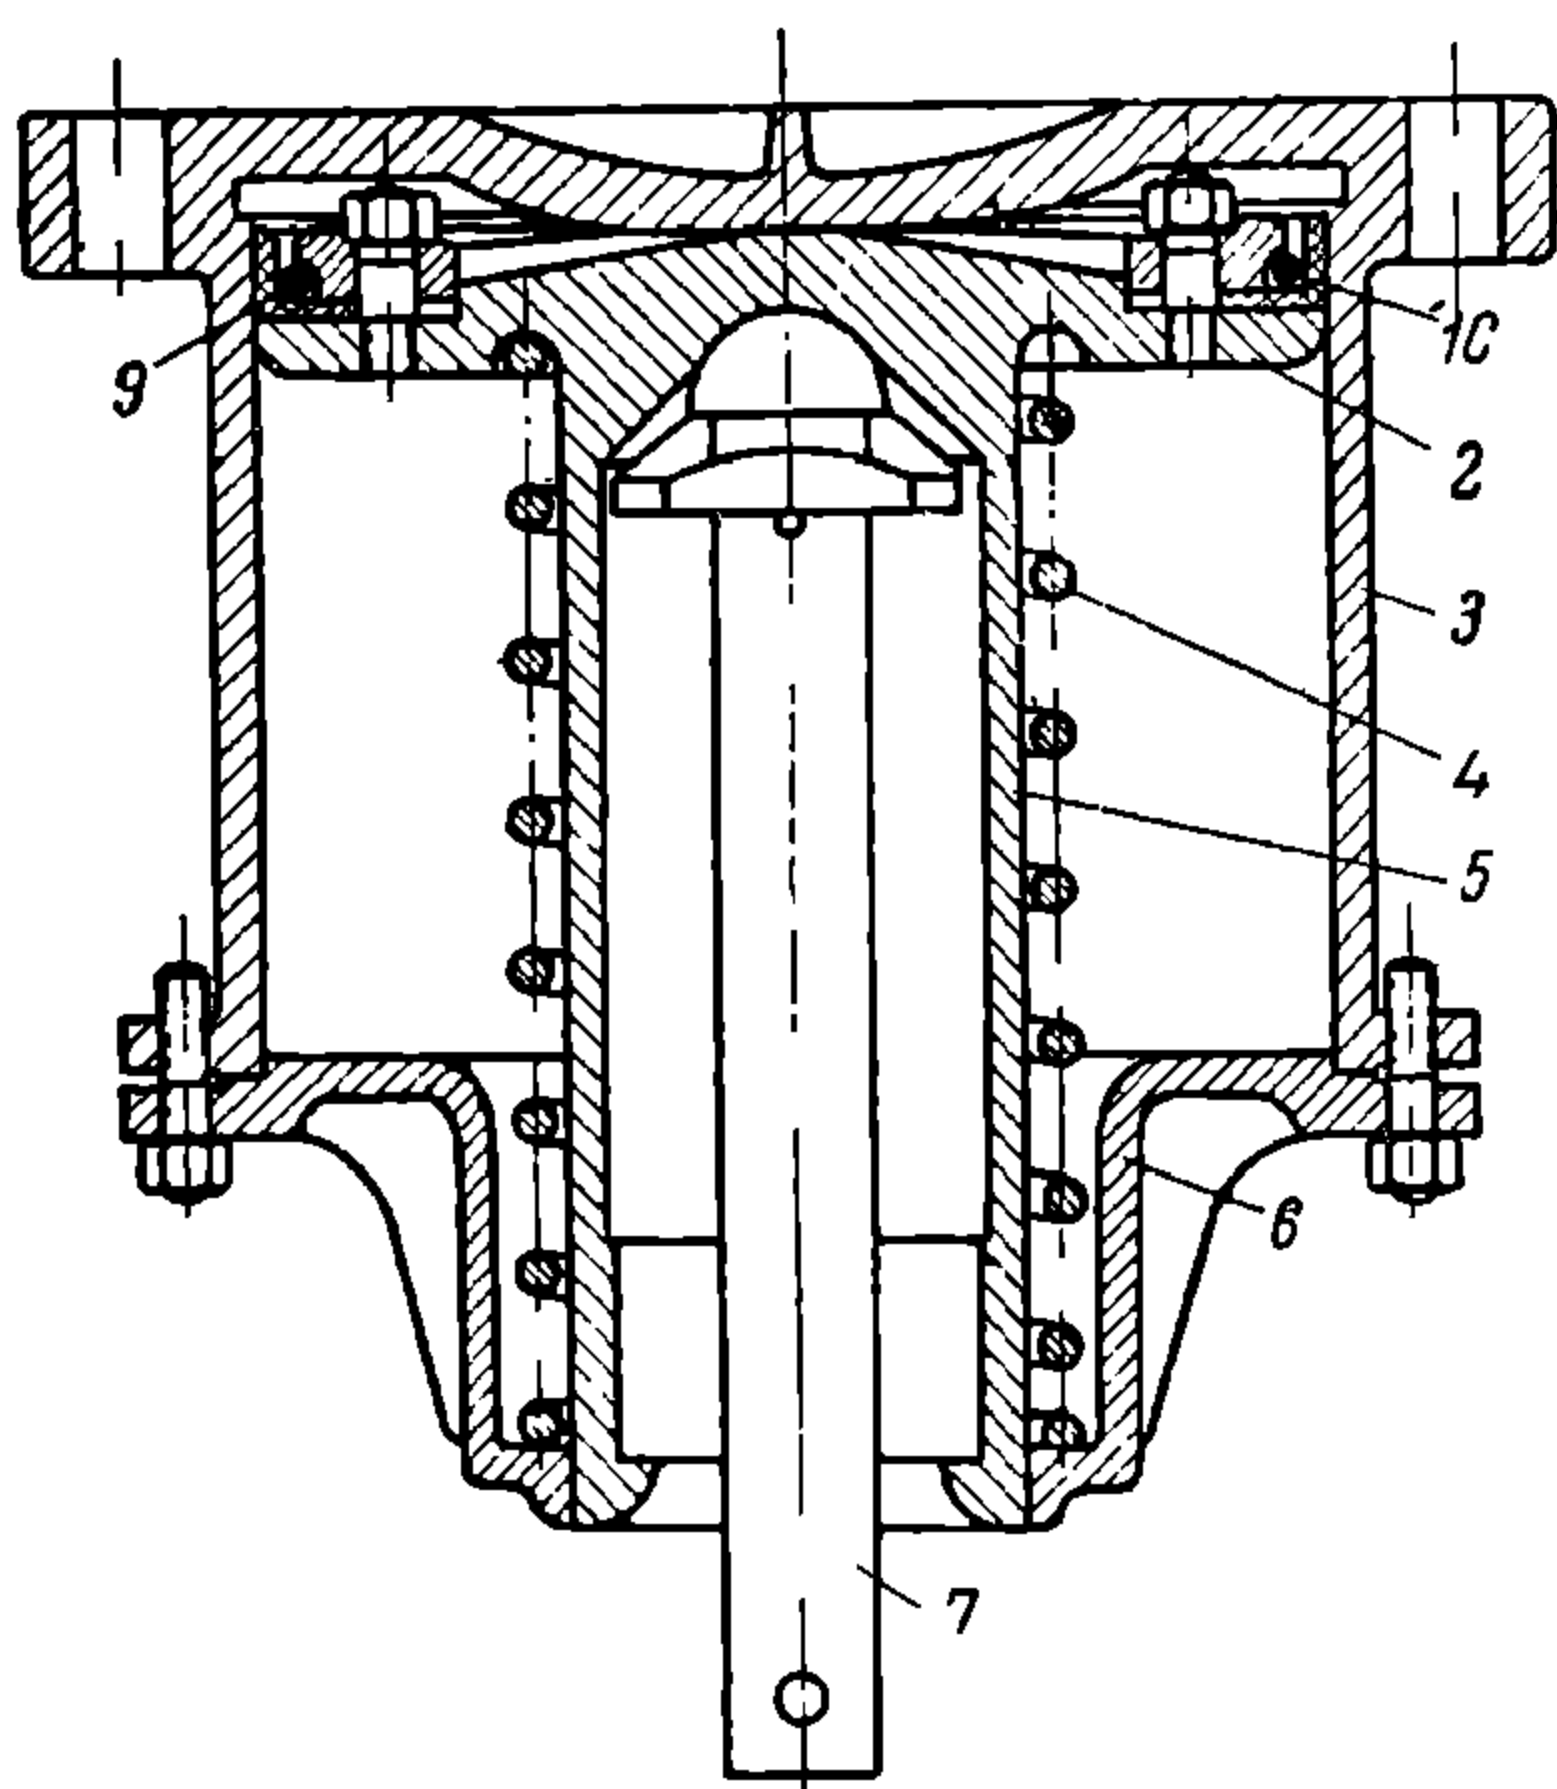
Горизонтальный тормозной цилиндр с местом для воздухораспределителя.
